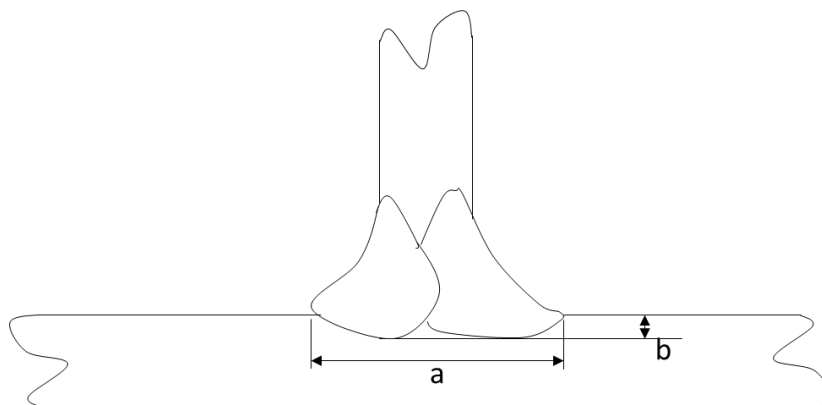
Dimensões da geometria geral das soldaduras
